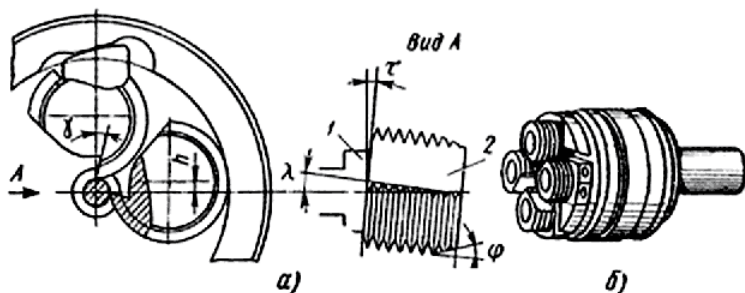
Резьбонарезная головка с круглыми гребенками:
